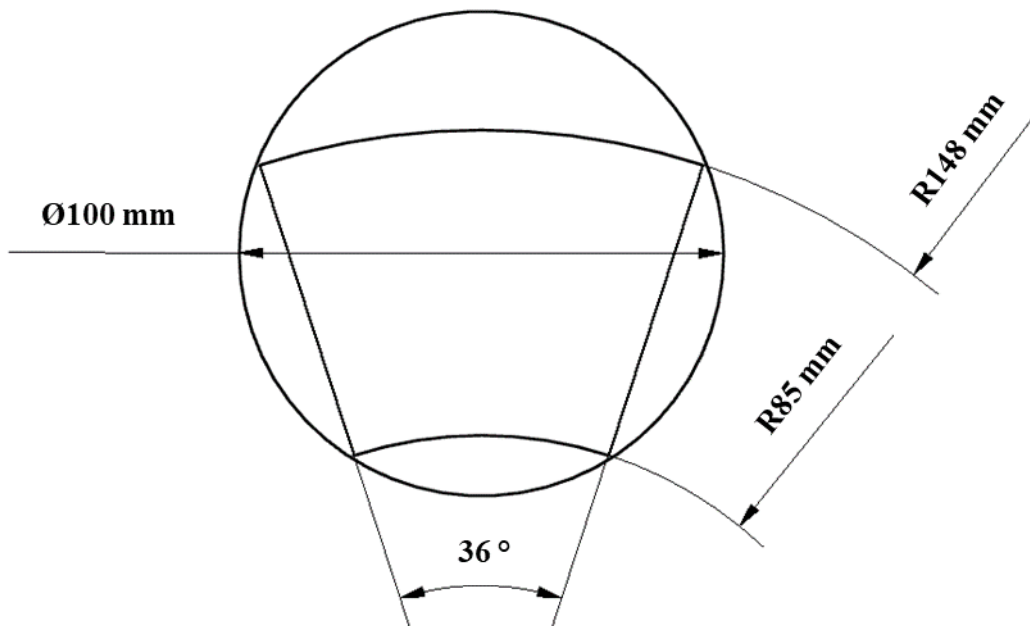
Dimensions des pastilles du rotor que l'on peut découper dans un disque de 100 mm de diamètre.
